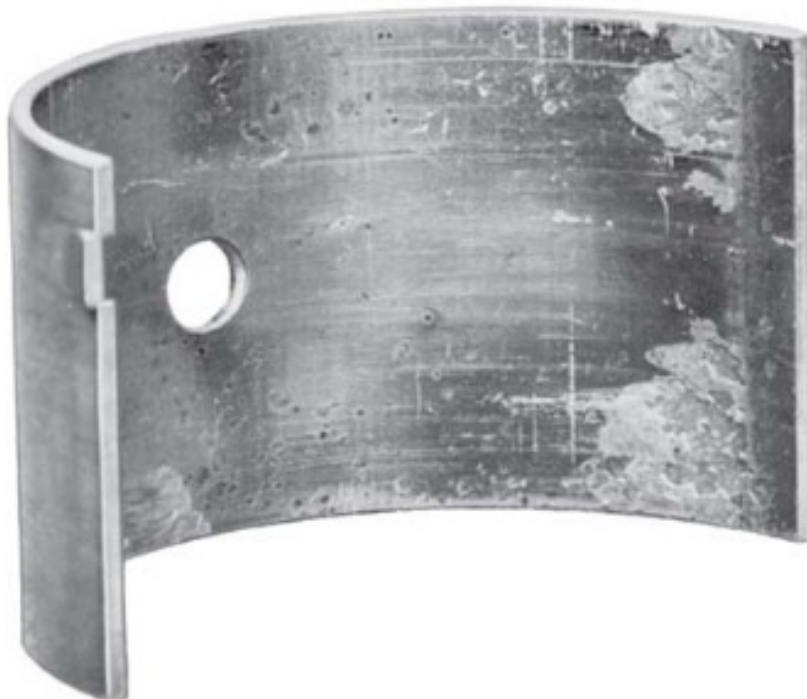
Desgaste excesivo en el extremo del cojinete.
